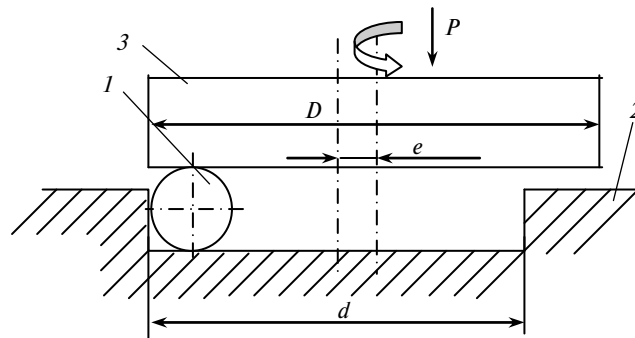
Схема накочування сферичної заготовки плоскими поверхнями: 1 – сферична заготовка; 2 – циліндрична камера; 3 – обертовий інструмент.
